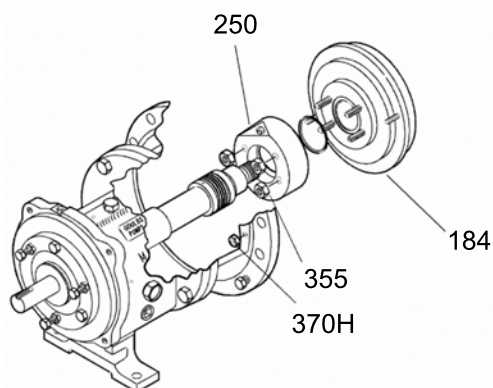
Extracción de la carcasa del rodamiento y del rodamiento
